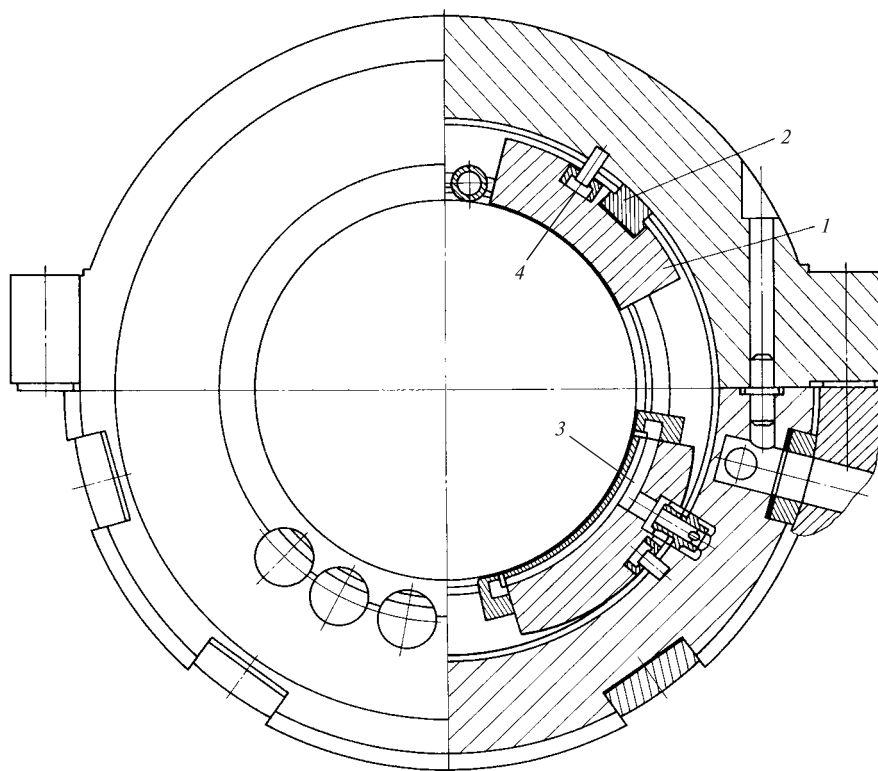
Опорный вкладыш подшипника турбин ЛМЗ
